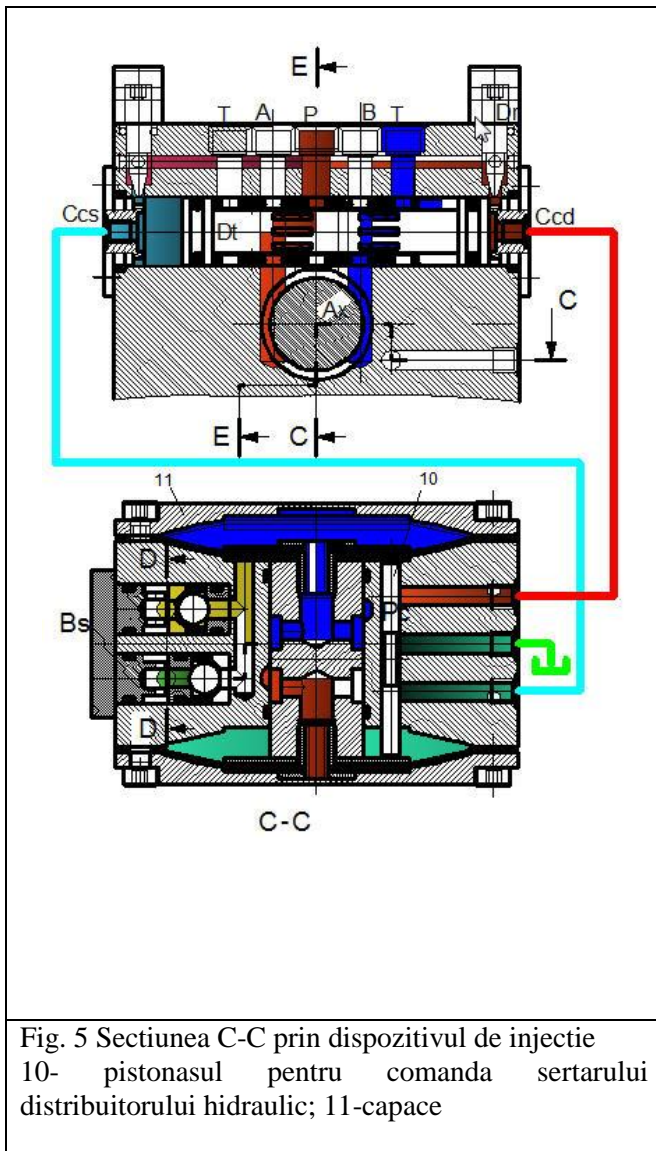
Sectiunea C-C prin dispozitivul de injectie
